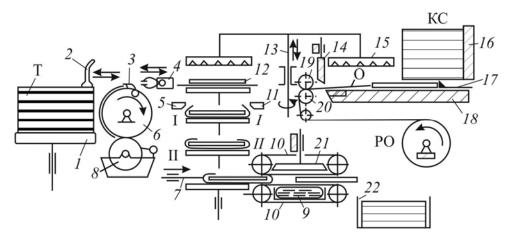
Схема листового крышкоделательного автомата: 1, 16 — магазины; 2 — присосы; 3 — клапаны; 4 — щипцы; 5, 11 — загибающие планки; 6 — цилиндр; 7 — выталкивающая планка; 8 — клеевой аппарат; 9 — резиновая подушка с водой; 10 — транспортер; 12 — сборочный стол; 13 — ось головки с присосами; 14 — ножи; 15 — двойная головка с присосами; 17 — толкатели; 18 — стол; 19, 20 — ролики; 21 — прессующая плита; 22 — приемный стол; Т — покровный материал; РО — рулон отстава; КС — картонные сторонки; О — отстав
